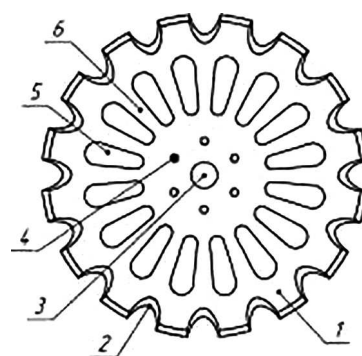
Схема сферического диска почвообрабатывающего орудия:
